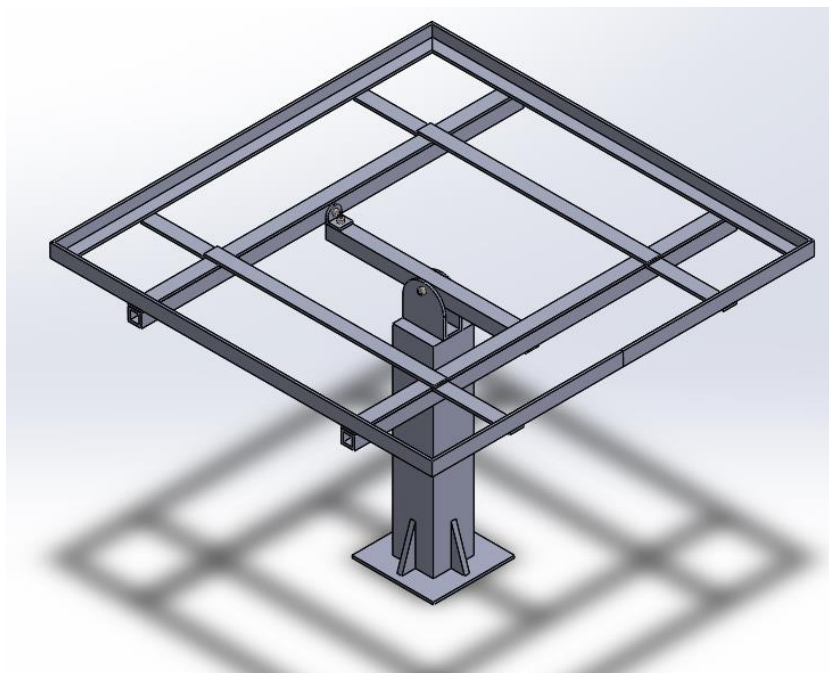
Desenho CAD da montagem do suporte em U sobre a base antiga.
